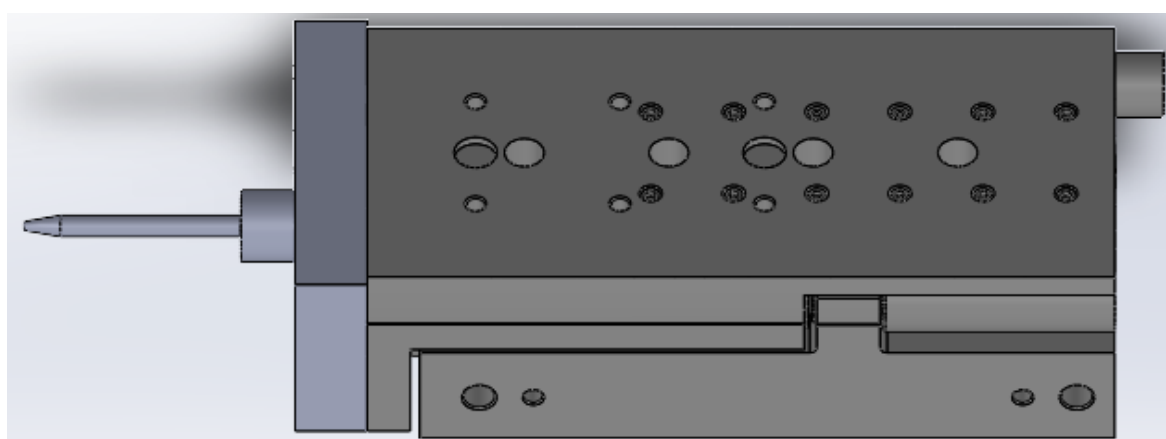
Фронтальный сварочный контур
